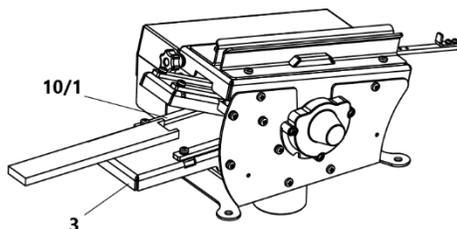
Настройка приставки для обработки планки верхней
